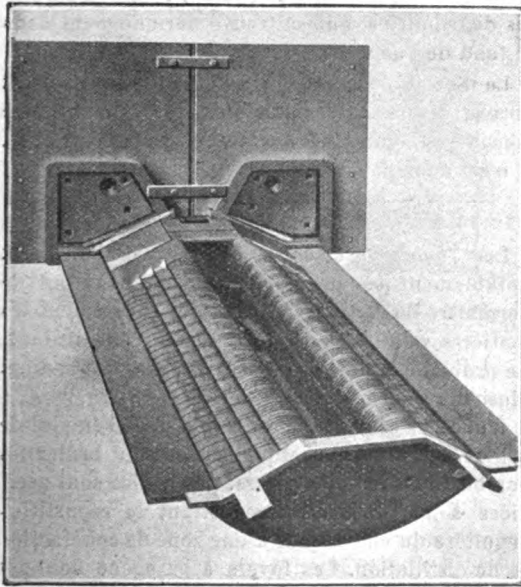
VUE ARRIÈRE DU STOKER, CLASSE D.
